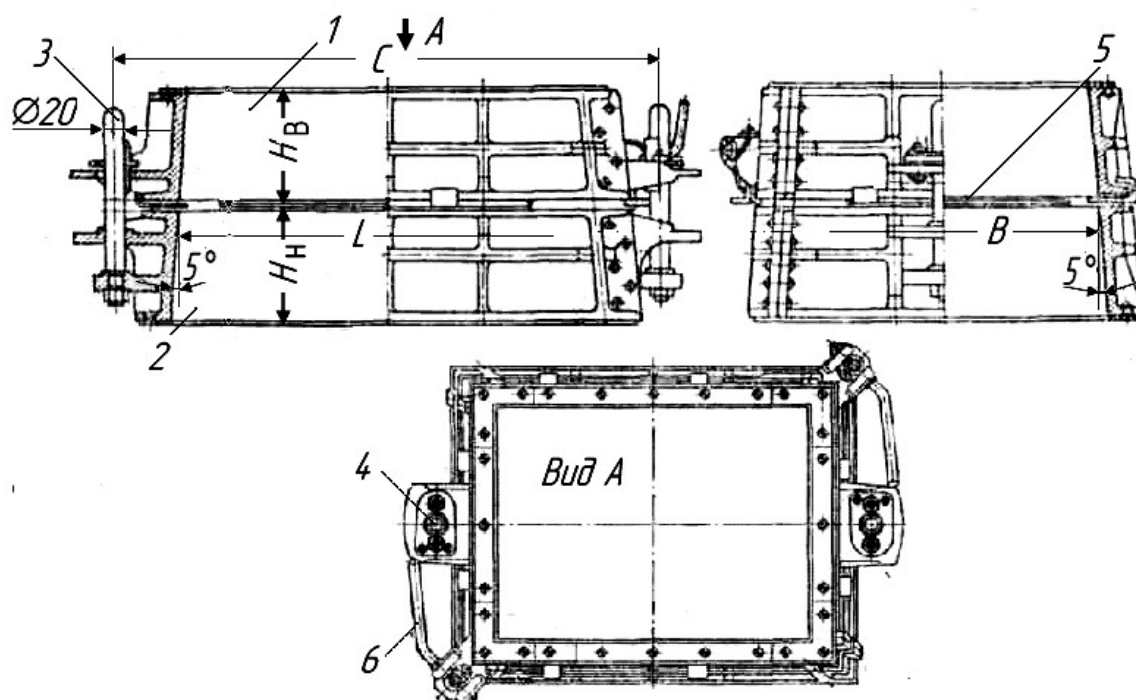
Съемная монтированная опока для безопочной формовки: 1 – верхняя половина; 2 – нижняя половина; 3 – штырь; 4 – втулка; 5 – нож; 6 – рычаг ножа
